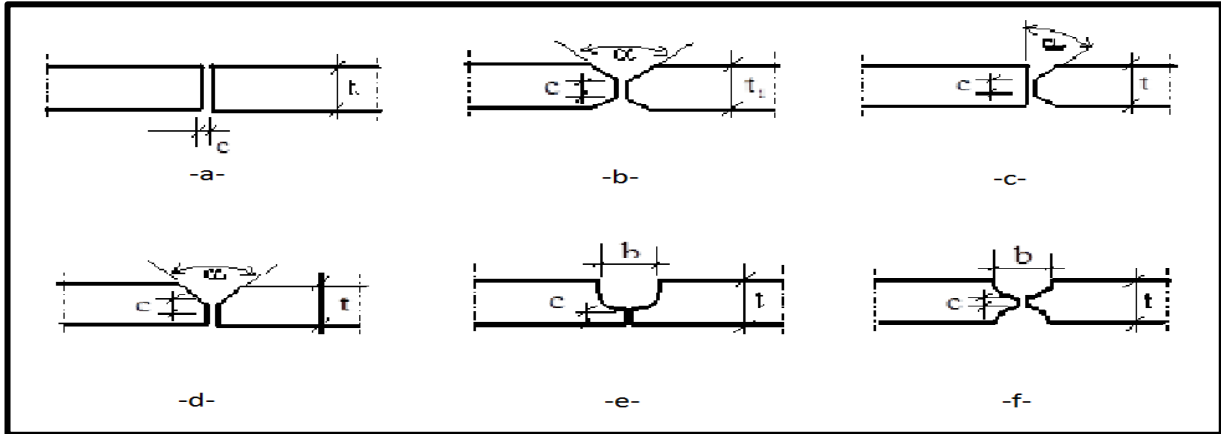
Chanfreins des bords pour les soudures bout à bout.
